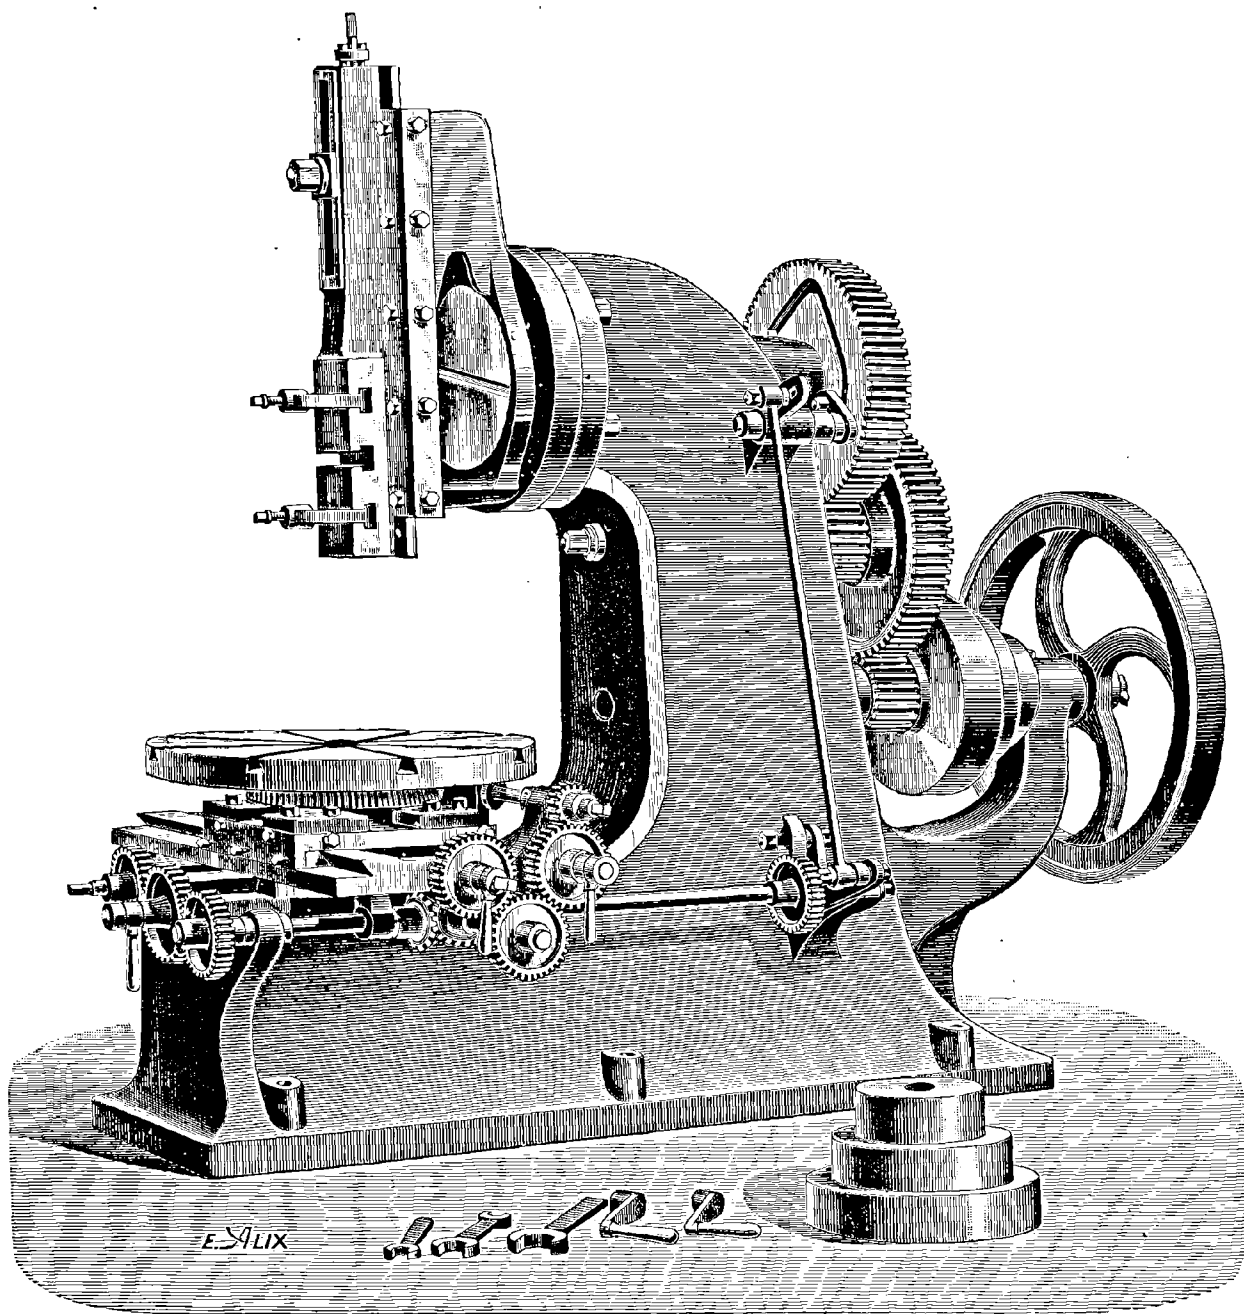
Machine à mortaiser à tête inclinable de M. L. Besse.
